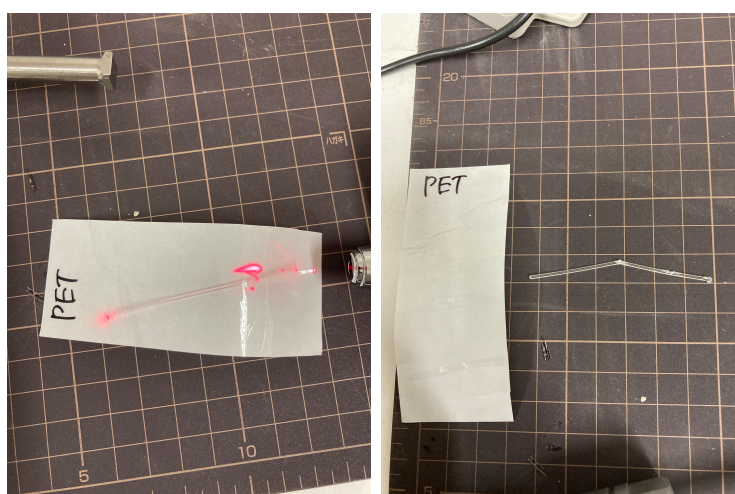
PET シートに溶着試験した前後のファイバーの比較:左が溶着前、右が溶着後
